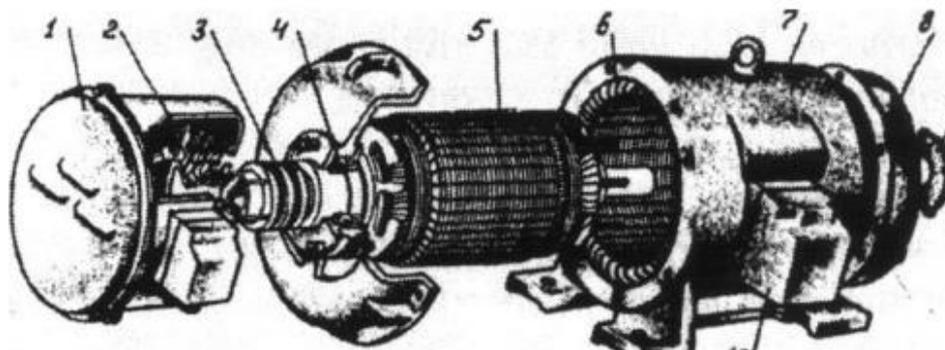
Асинхронный двигатель с фазным ротором в разобранном виде: 1. Крышка со стороны, где расположены контактные кольца и щетки; 2-щеткодержатель и щетки; 3 - контактные кольца; 4-й подшипник; Стальной сердечник 5-го ротора (трехфазная катушка на его пластине); 6-катушка статора; 7-й корпус; 8-опорный щит; Крышка подшипникового щита со стороны 9-го вала, соединенного с механизмом; 10-я обмотка статора представляет собой коробку с выводными концами.
